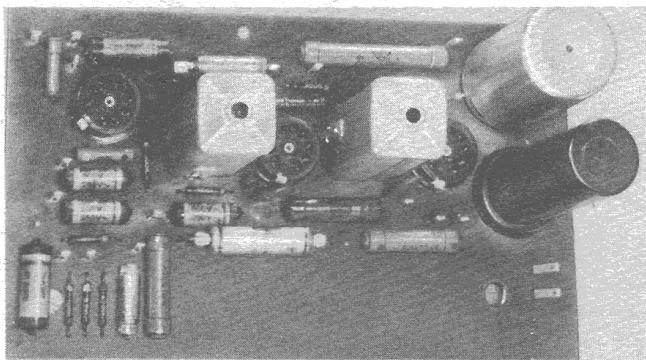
Blick auf die Montageplatte mit Sockeln für die beiden Zf- und die Nf-Doppelröhre, mit Bauelementen, Filtern, Doppel-Elektrolytkondensator und Trockengleichrichter
